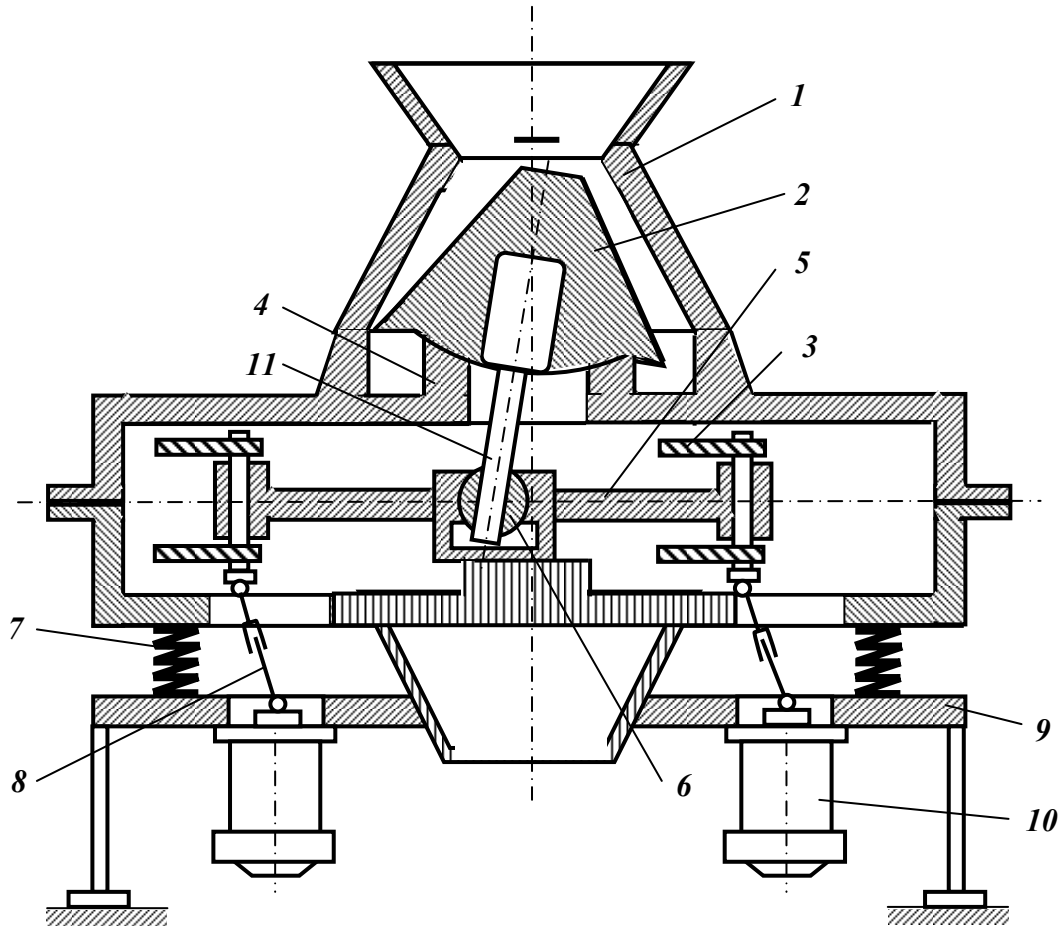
Схема конусної інерційної дробарки типу КІД.
